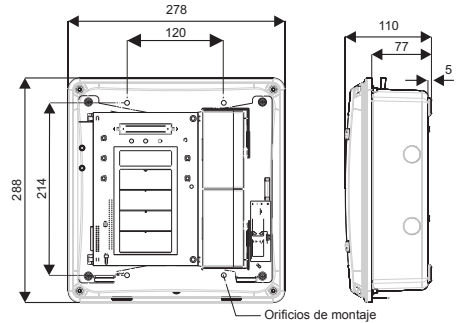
Vista dimensional del Gasmaster con sus orificios de montaje
